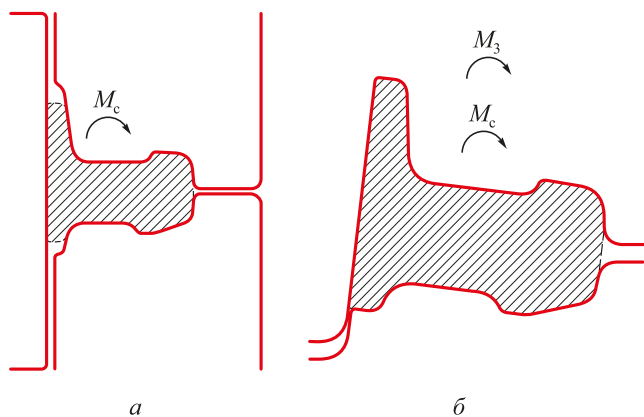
Общий вид универсального трехвалкового (а) и чистового двухвалкового (б) калибров для прокатки рельсов острогового
